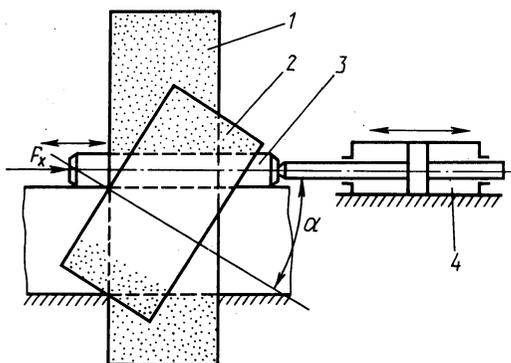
Схема бесцентрового врезного шлифования с осциллирующим перемещением изделия: 1 — шлифовальный круг; 2 — ведущий круг; 3 — обрабатываемая деталь; 4 — гидроцилиндр выталкивателя
